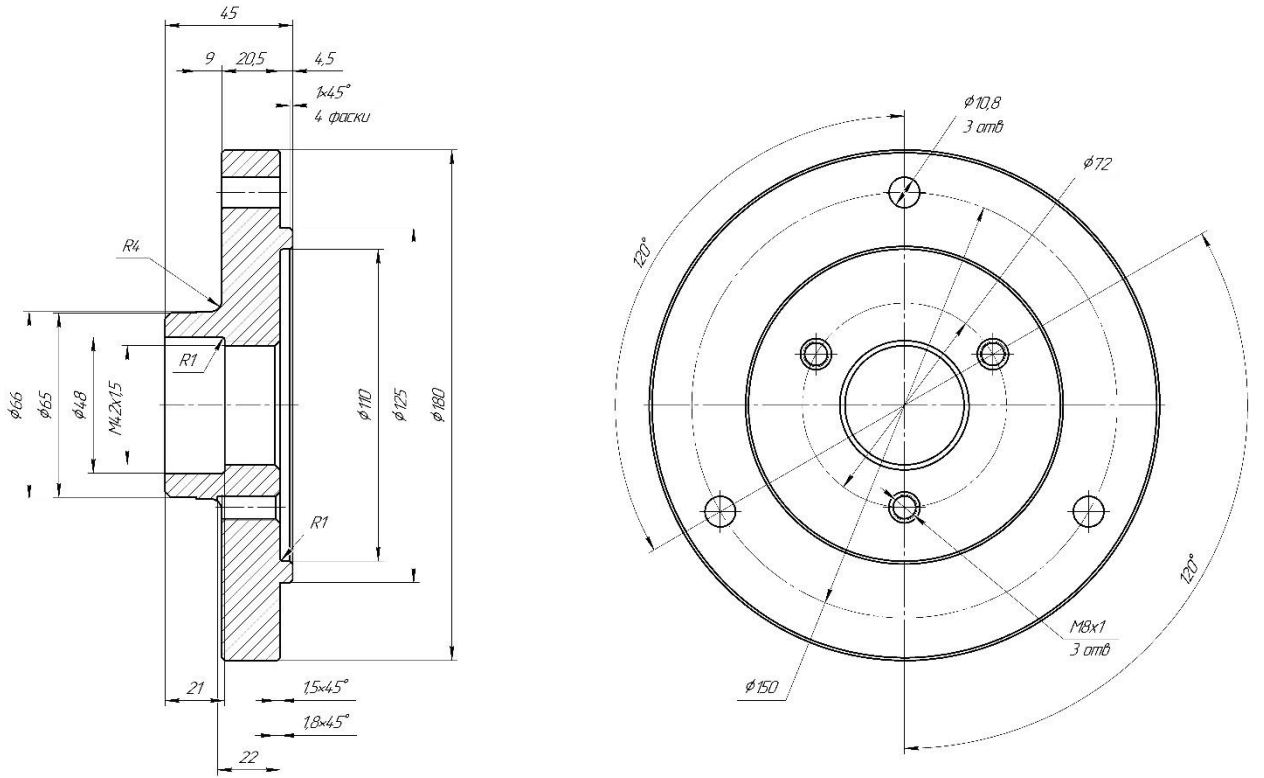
Креслення фланця шпинделя верстата 1П611
